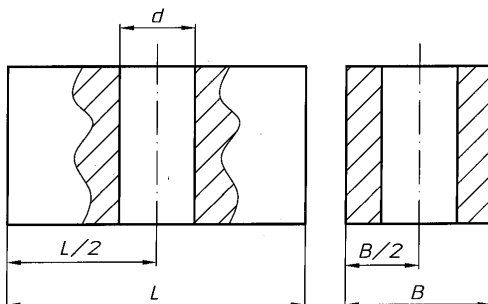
Обозначения размеров заготовки и обрабатываемого отверстия
